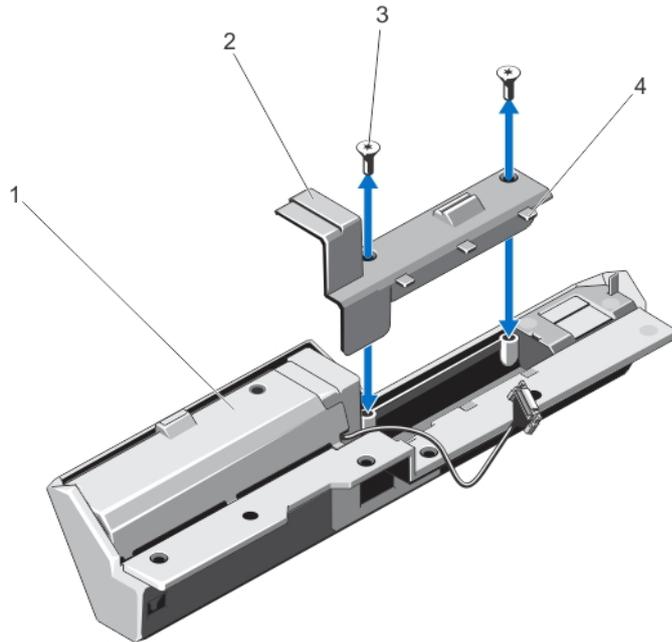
Extracción e instalación de la cubierta de la puerta de la caja para PCIe
